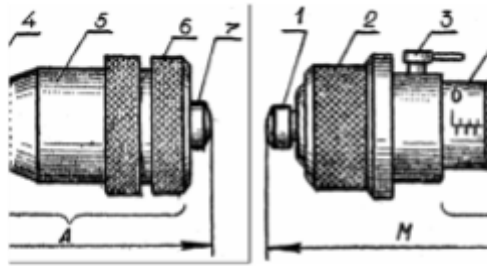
Мікрометричний нутромір: 1 – нерухомий наконечник; 2 – захисний ковпачок; 3 – стопор; 4 – стебло; 5 – барабан; 6 – ковпачкова гайка; 7 – мікрометричний гвинт
